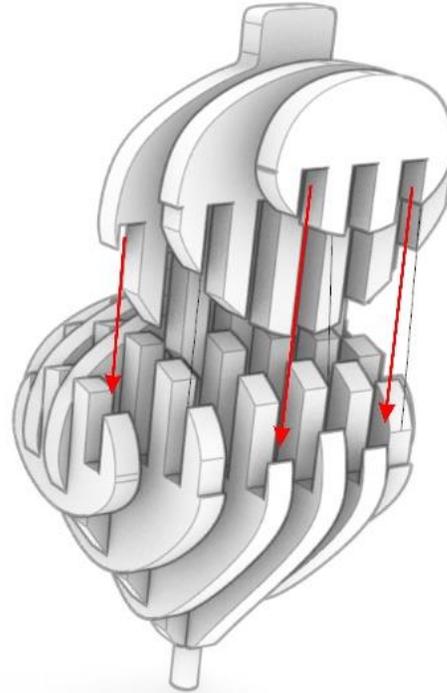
Planos técnicos propuesta: 2. Plano seriado cruzado. Elaboración propia.
